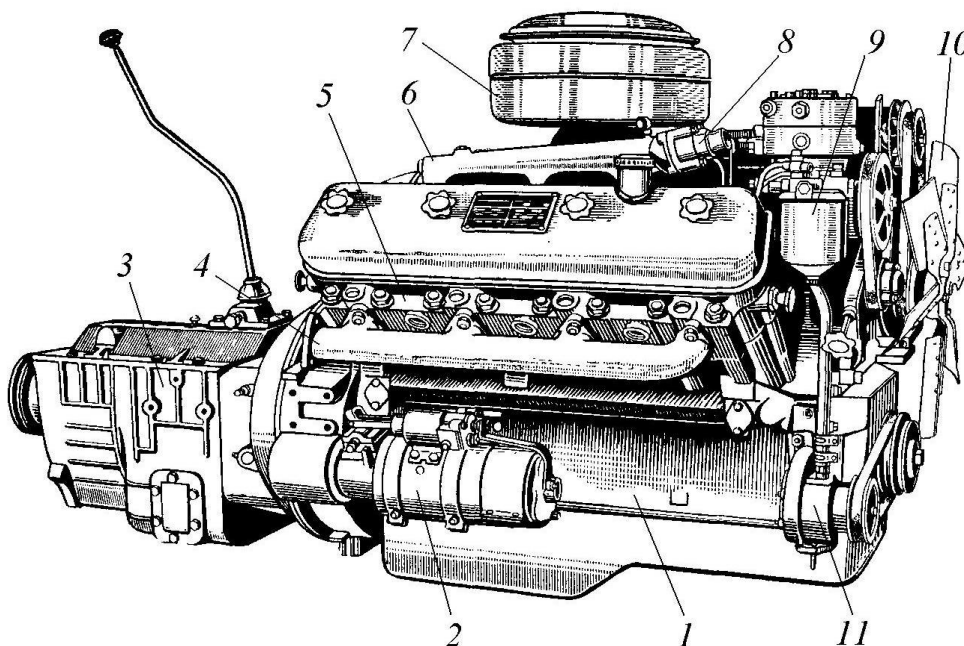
Загальний вид двигуна 8ЧН13/14
